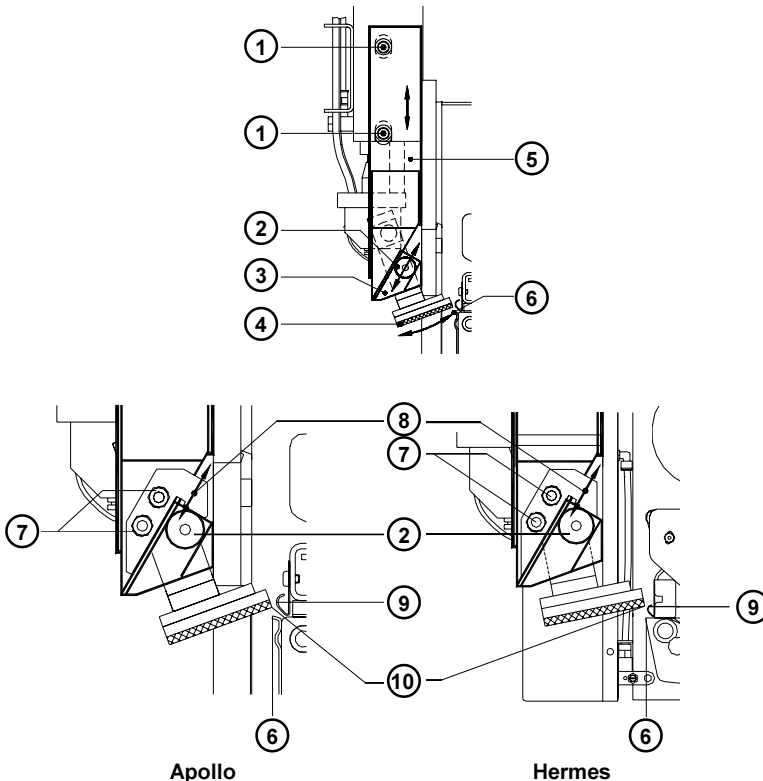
Justage der Schwenkbewegung des Saugblocks
